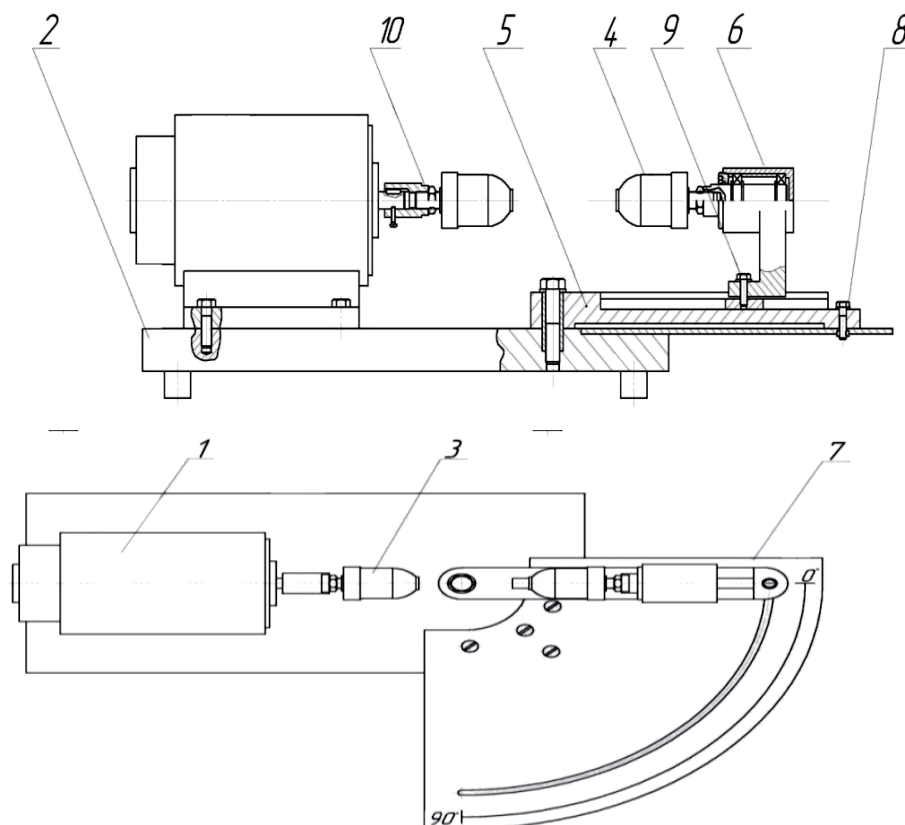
Схема стенда для испытаний полимерных подошвенных материалов на многократный изгиб
